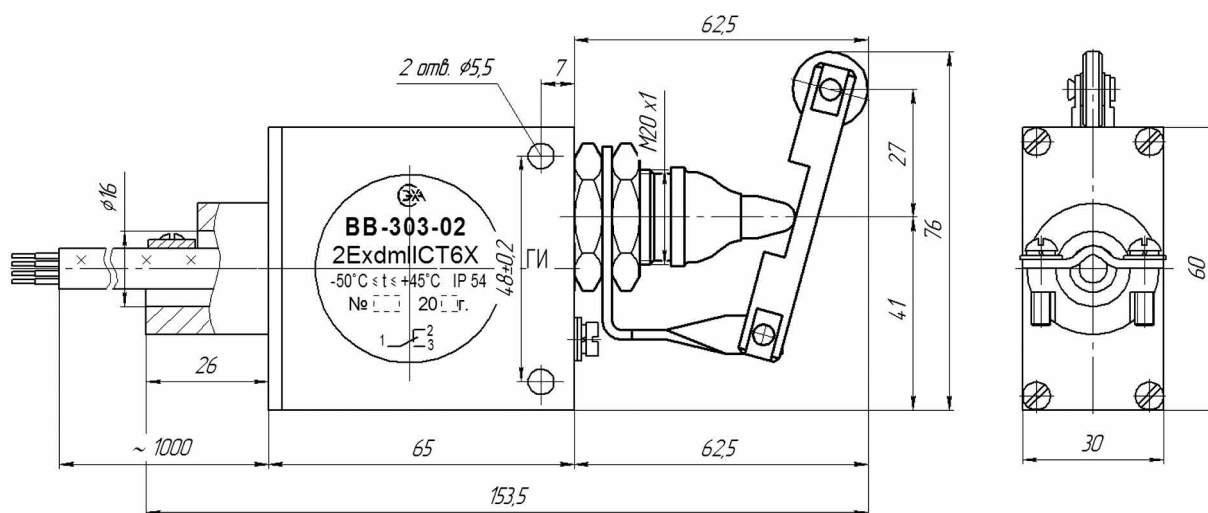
в. Габаритные и установочные размеры ВВ-303-02
